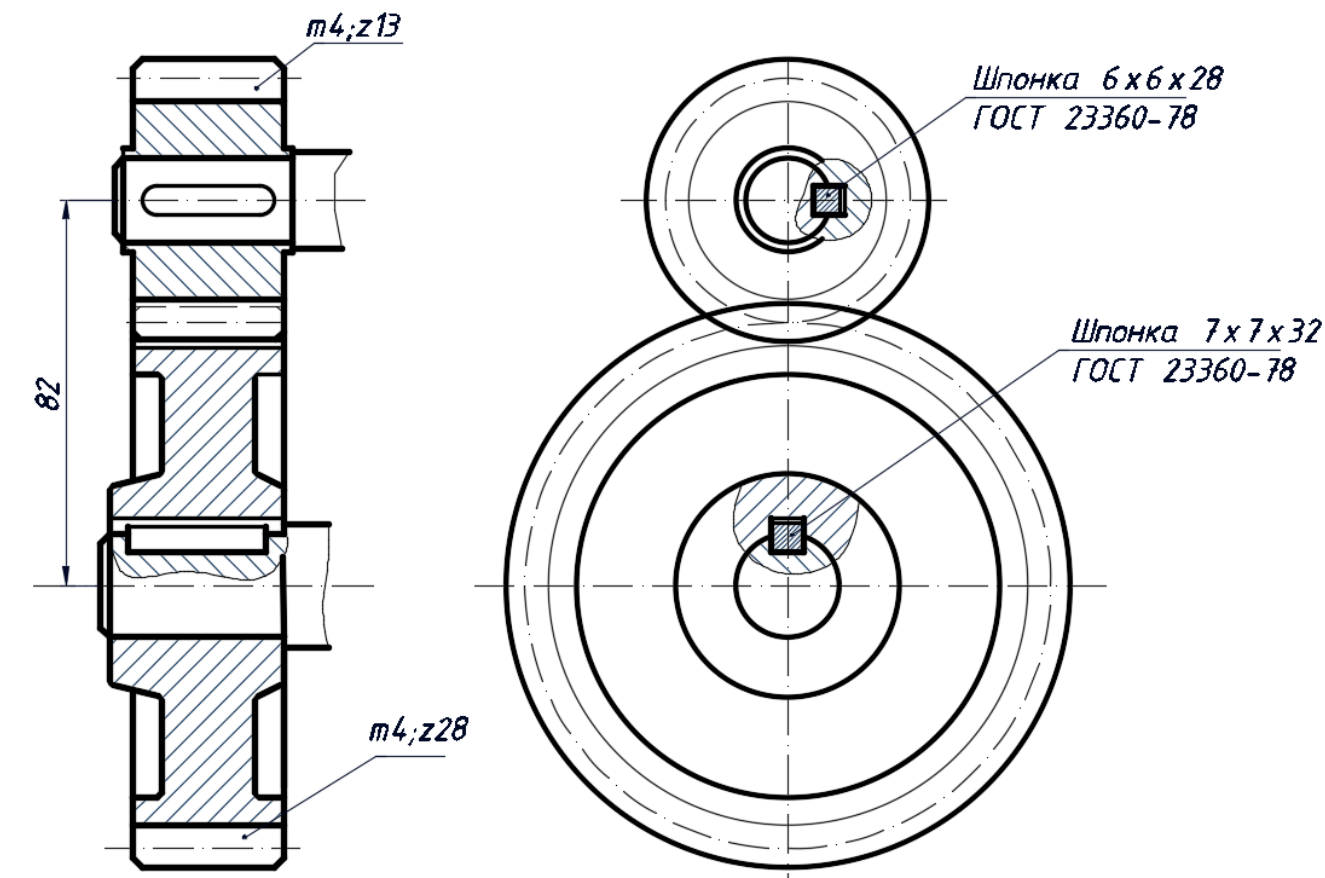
Образец выполнения чертежа зубчатого зацепления.
